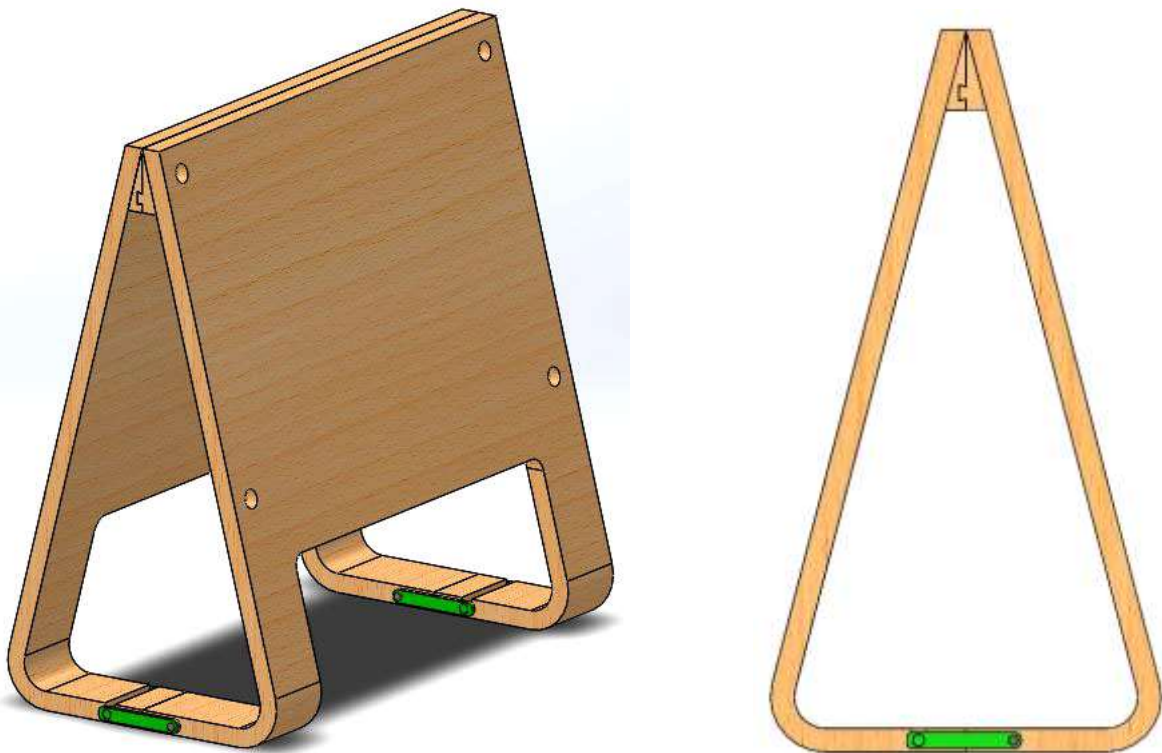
Ensamblaje ALL PLAY para embalaje primera opción
